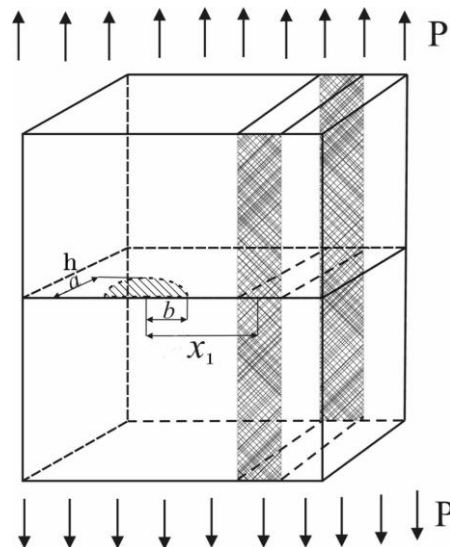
Схема розтягу товстої пластини з поверхневою напівеліптичною тріщиною біля зварного шва.
